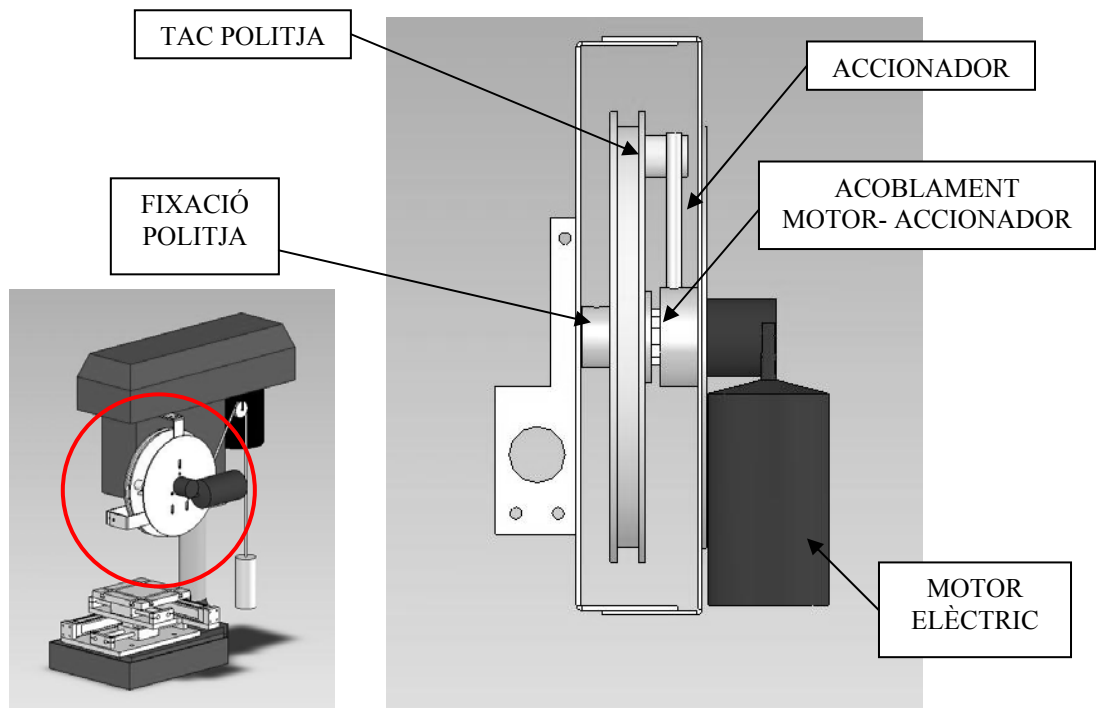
, a l'esquerra vista isomètrica de la màquina i a la dreta vista inferior del conjunt.
